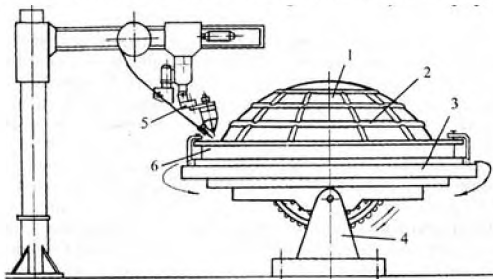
Схема установки для сварки полушеры со шпангоутом: 1 - днище; 2 - приспособление; 3 - стол манипулятора; 4 - манипулятор; 5 - сварочный автомат; 6 - шпангоут днища
